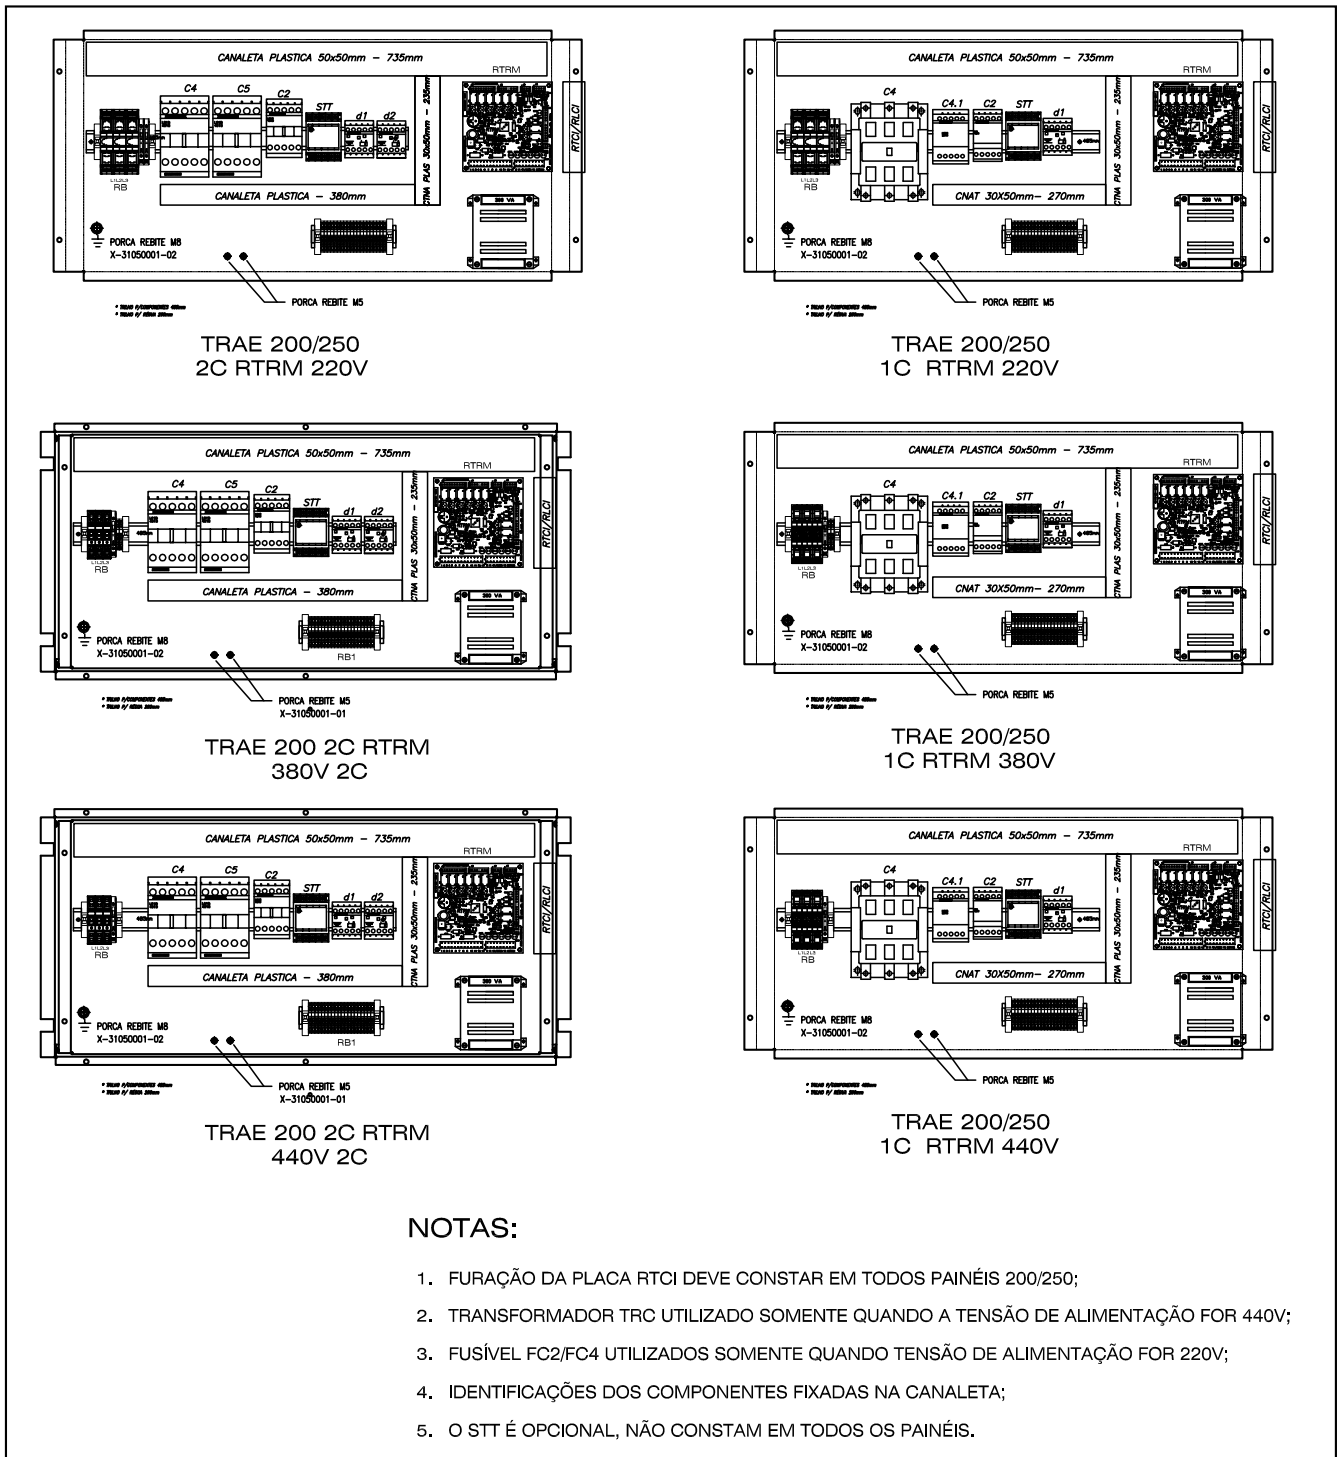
Layout de Quadros Eléctricos TRAE (Padrão)
